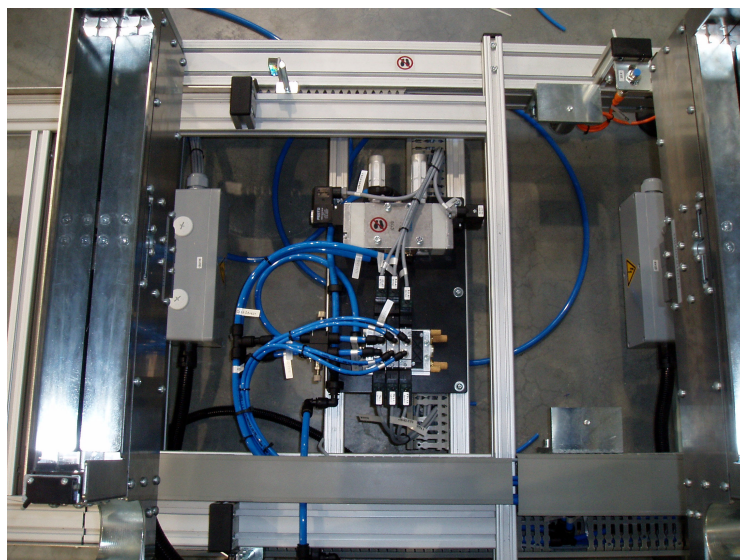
Zakreslené zapojení senzorů (interní dokumentace firmy Engel)
